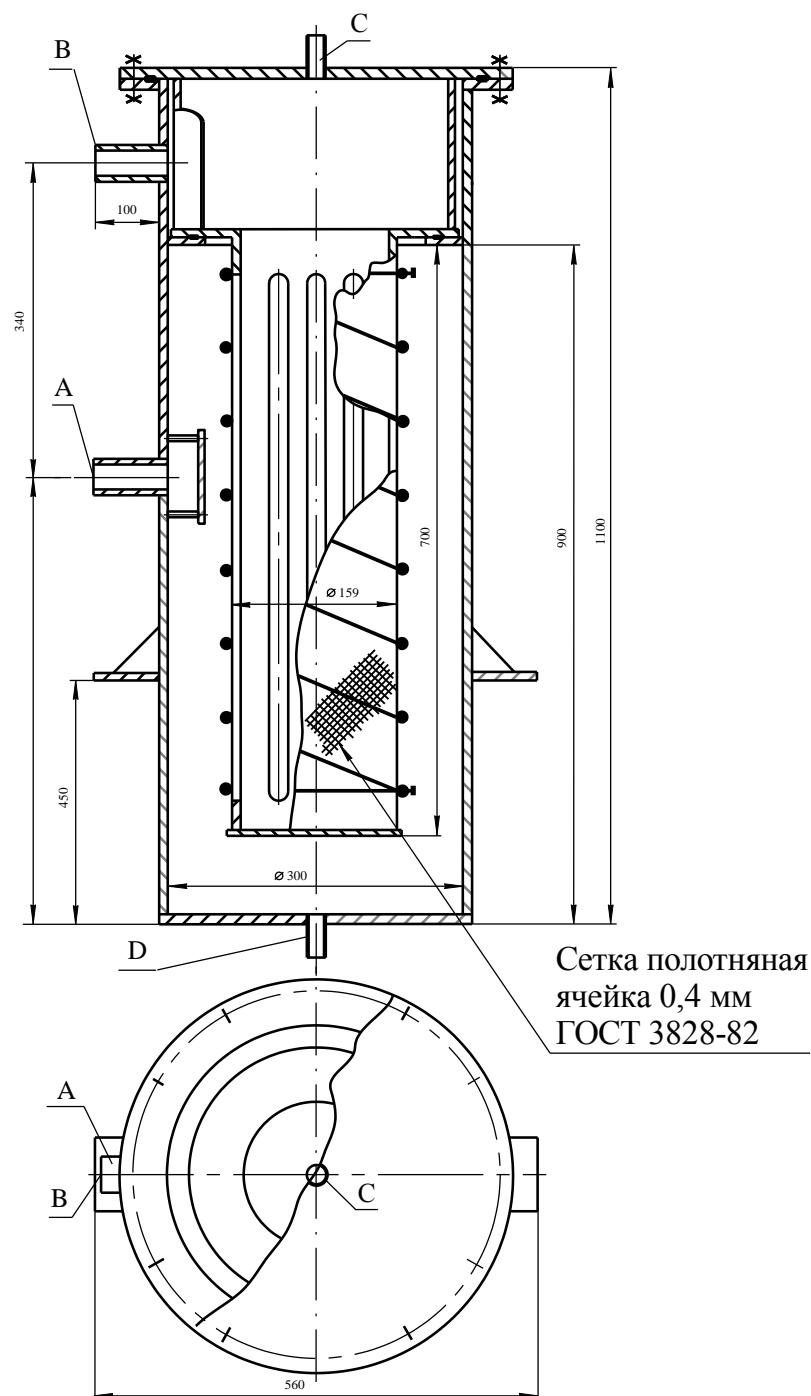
Габаритный чертеж фильтра фосфата QCT10AT001
